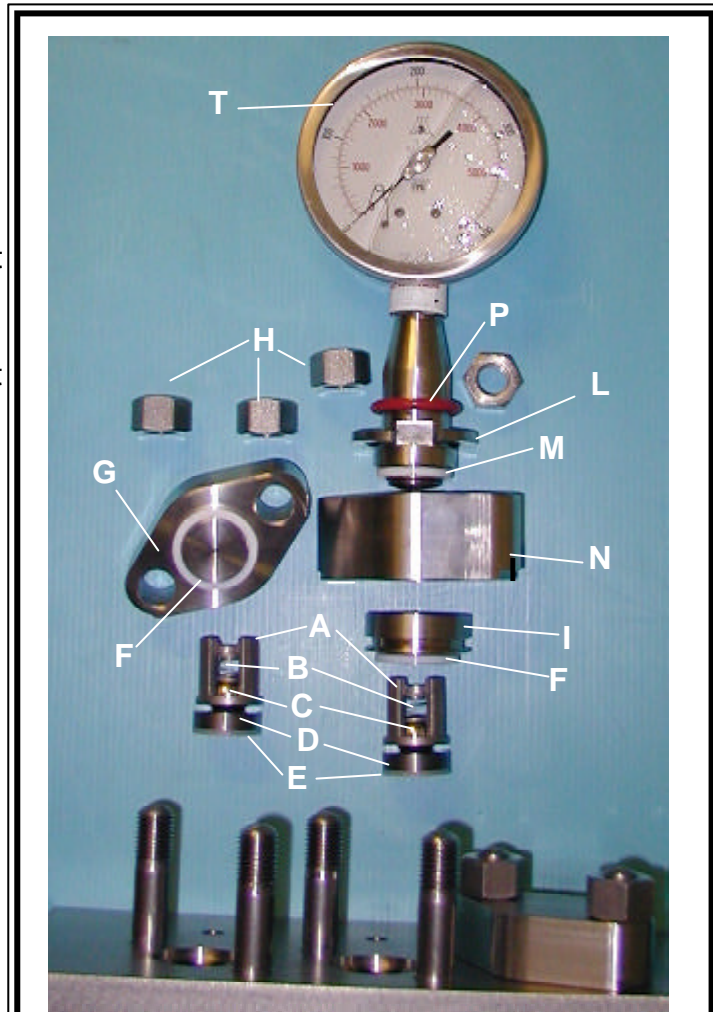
Explosionszeichnung der Ventilgruppe Ausgang -
